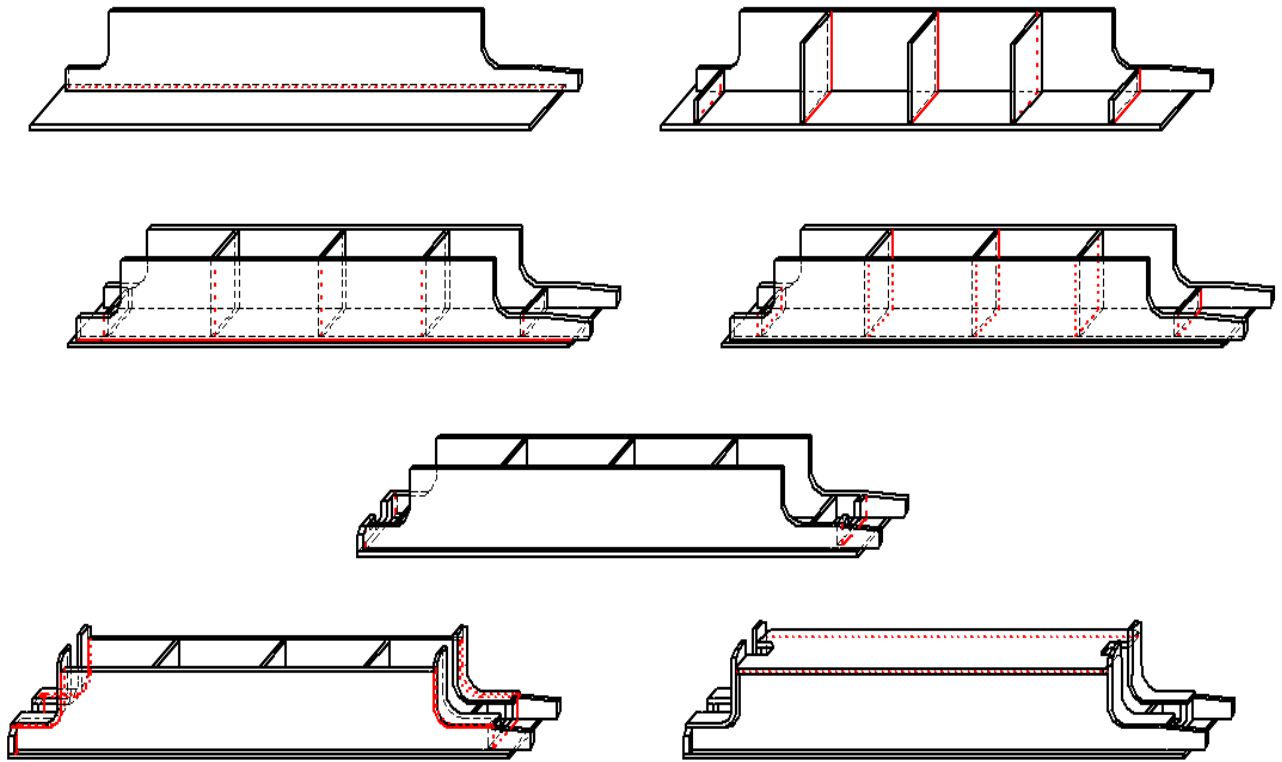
Предлагаемая технология сборки и сварки балки концевой рамы тележки крана
